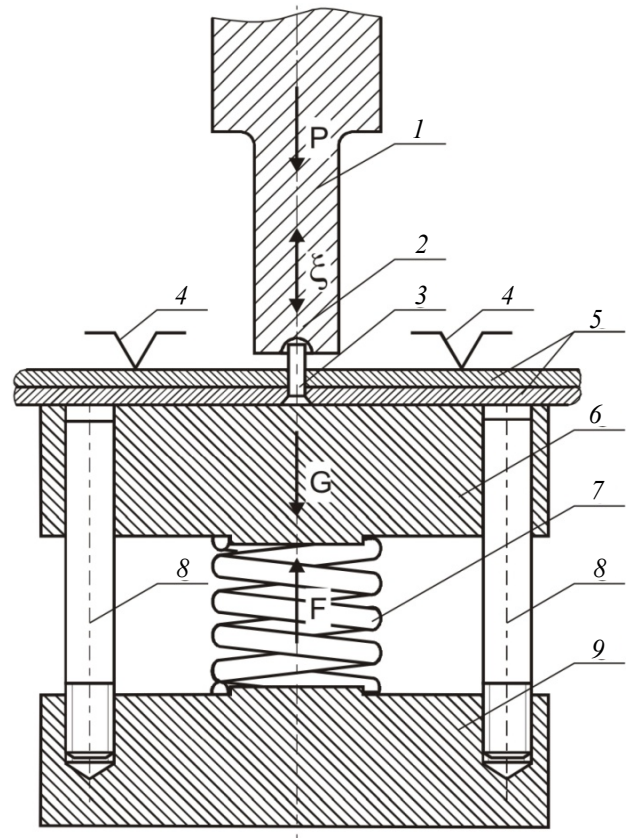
Схема образования заклепочного соединения: 1 – ультразвуковой излучатель; 2 – профилированная обжимка; 3 – заклепка; 4 – прижим; 5 – пакет соединяемых деталей; 6 – упор; 7 – пружина; 8 – направляющая; 9 – основание; P – сила прижима; F – сила упругости пружины; G – сила тяжести упора
